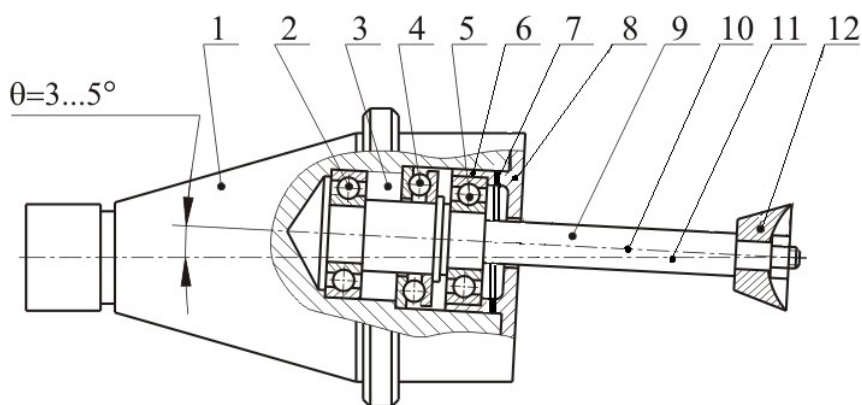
Пристрій для сферичного прошивання і дорнування циліндричних і фасонних отворів: 1 - корпус (оправка з конічним хвостовиком); 2, 5-радіальні шарико-підшипники; 3 - отвір оправки 1; 4 - упорний шарикопідшипник; 6 - втулка; 7 - компенсаційна пластина для натягу підшипників; 8 - кришка; 9 - інструментальний шпиндель; 10 - вісь інструментального шпинделю; 11 - вісь яка співпадає з віссю отвору, що оброблюється (шпинделю верстата); 12 - інструмент сферичного прошивання і дорнування отворів
